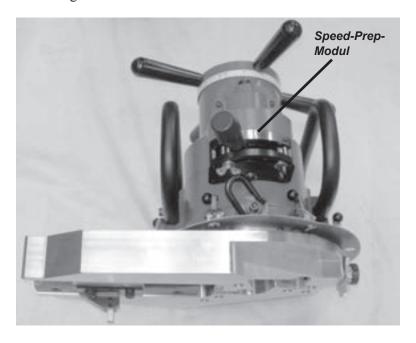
Der einschneidige Werkzeugschlitten verschiebt das Werkzeug radial entlang der Rohroberfläche. Er wird von einem Sternrad entlang einer Vorschubspindel angetrieben.
